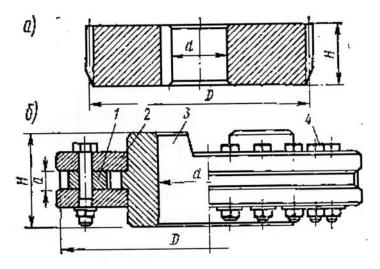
Инструмент для накатки зубьев шестерен: а — цилиндрический накатник со скосом в заборной части; б — сборный накатник; 1 — зубчатый вкладыш; 2 — реборда; 3 — муфты; 4 — болт
